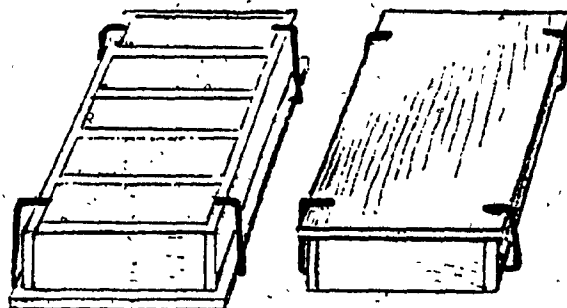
Méthode de moulage: châssis sens dessus dessous.
